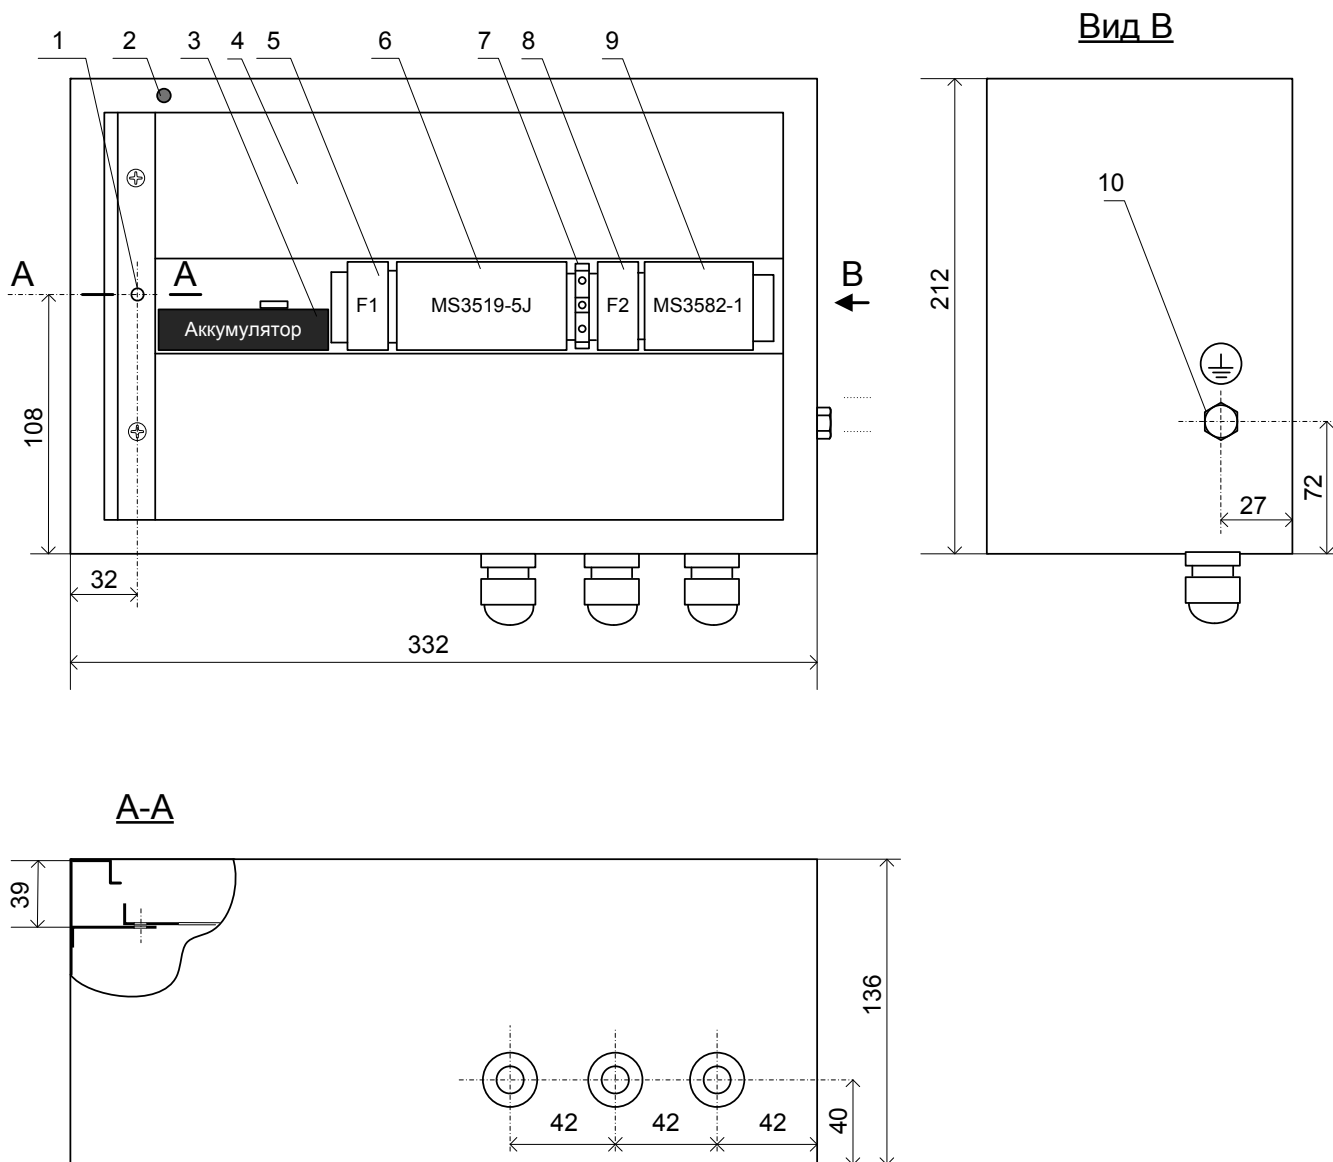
Внешний вид Модуля KD-01iRJ
